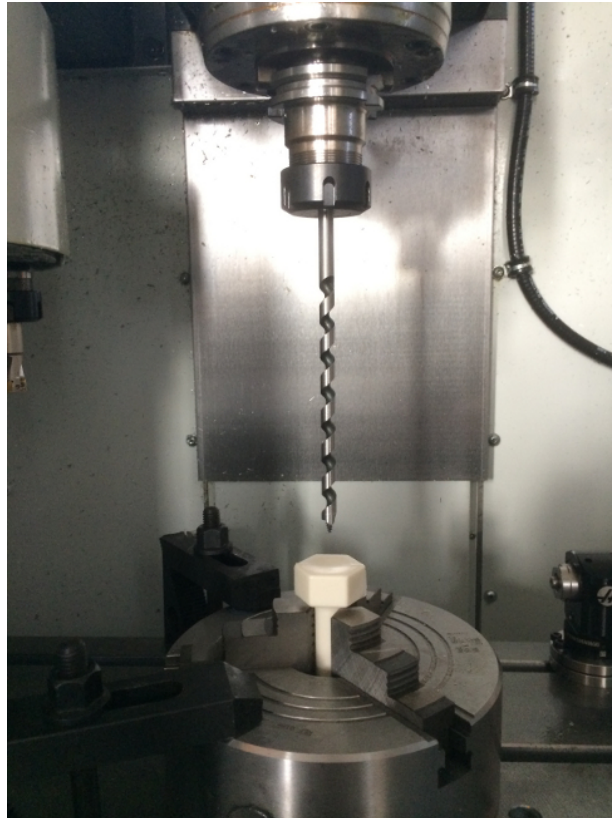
Dispositif de perçage des éprouvettes.
